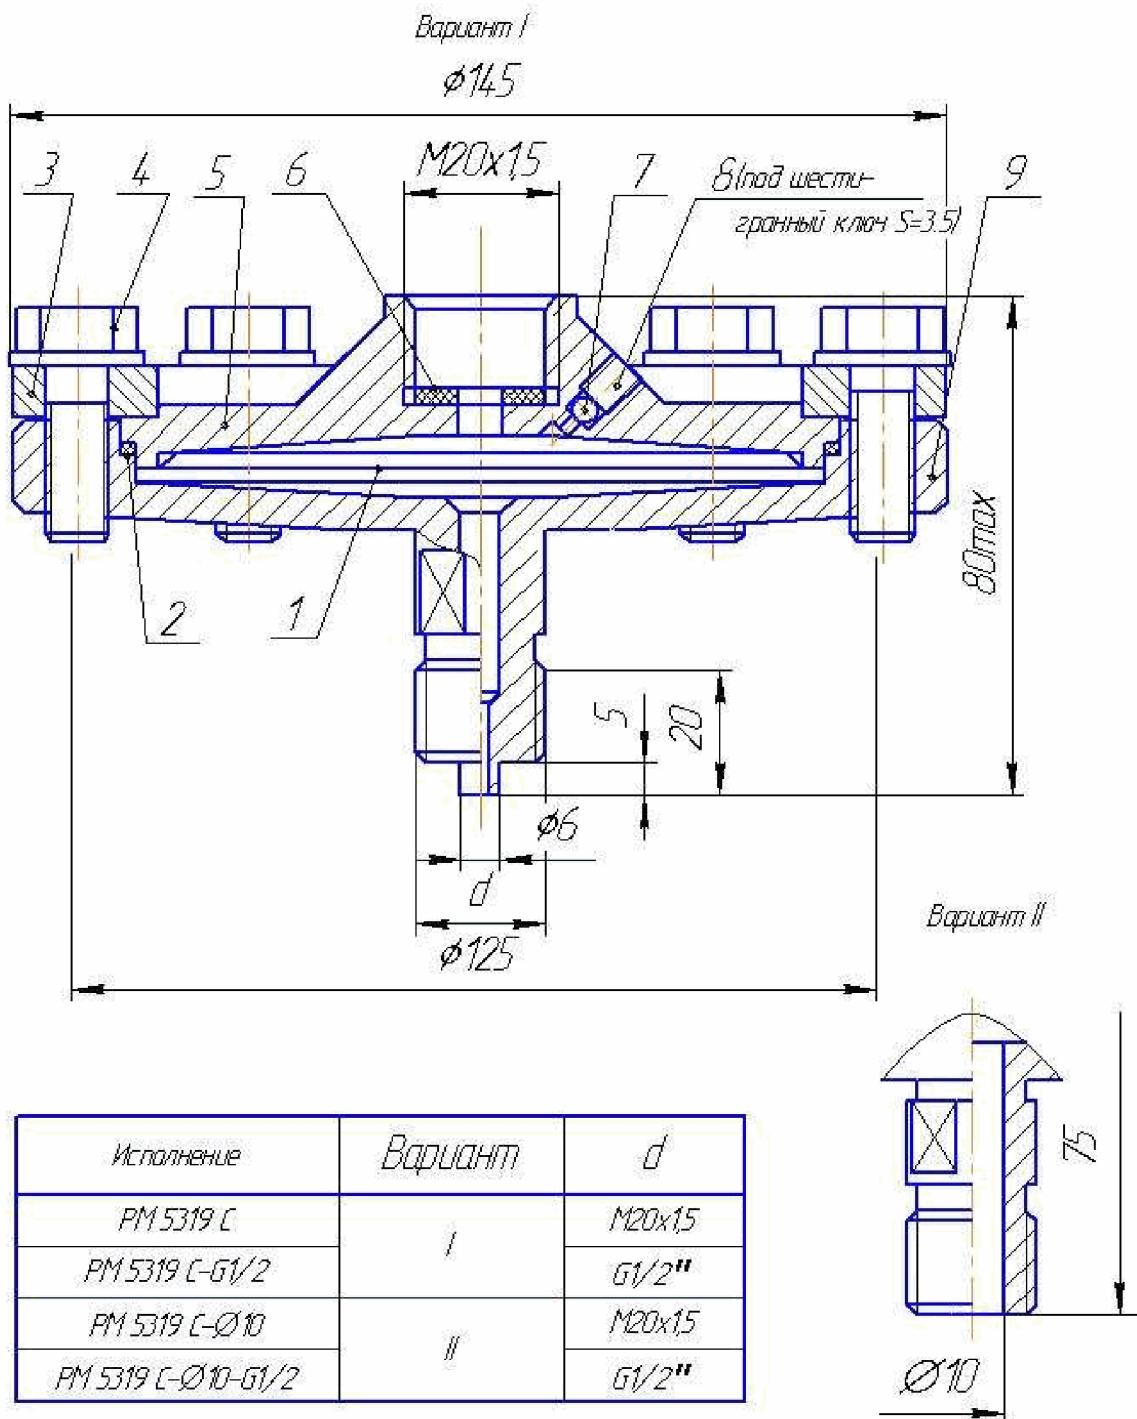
Конструкция, габаритные и присоединительные размеры
